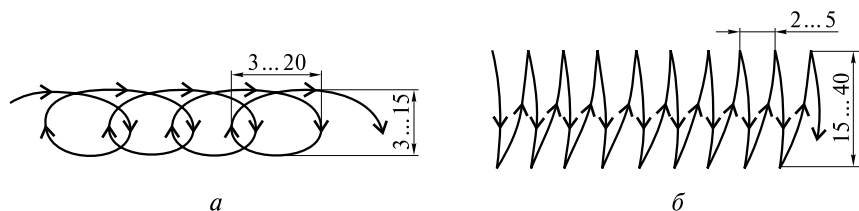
Колебательные движения электрода при сварке порошковой проволокой:
